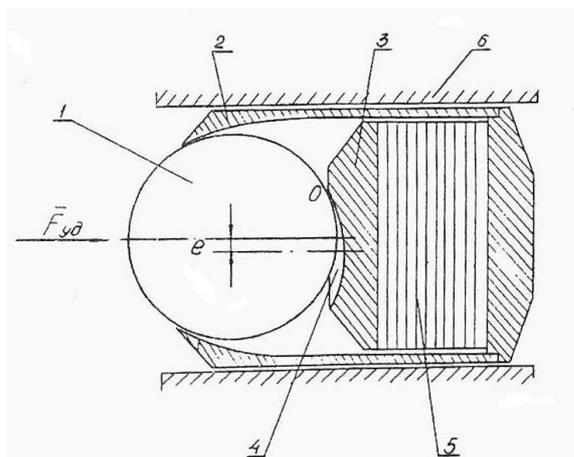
Устройство для квазипластического удара со смещенным сферическим углублением в головке 1- шар с закаленной сердцевиной; 2 – полый корпус; 3 – головка; 4 – сферическое углубление; 5 – демпфер; 6 – направляющая
